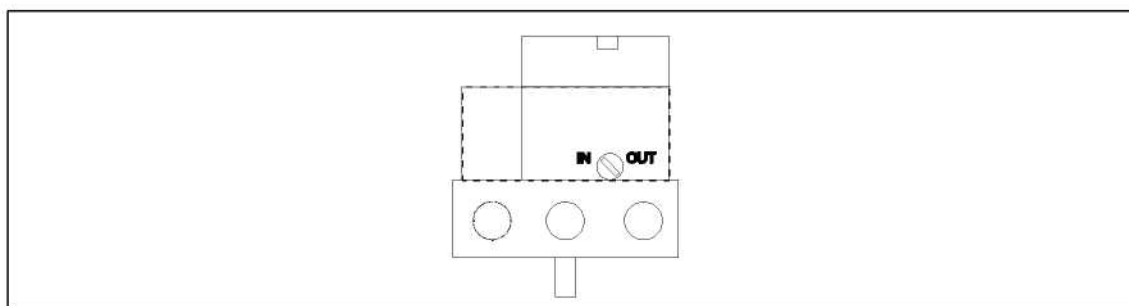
Переключатель продувочного воздуха на блоке клапанов, вид позиционера со стороны пневматических соединений при открытой крышке
